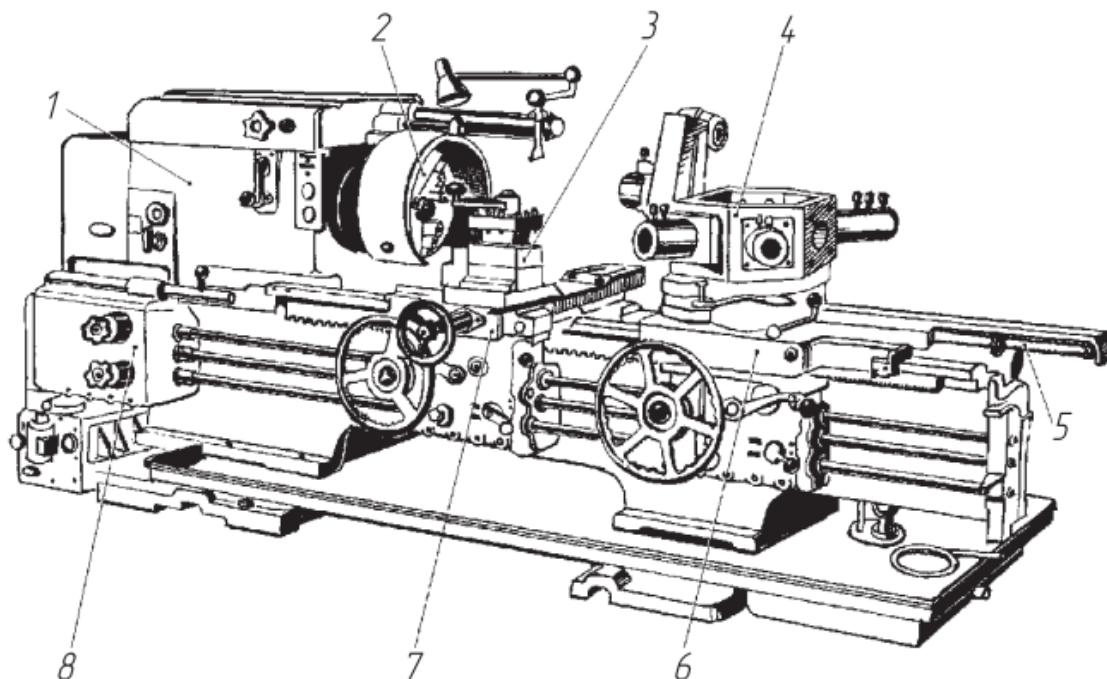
Токарно-револьверный станок модели 1П371: 1 – передняя бабка с коробкой скоростей; 2 – шпиндель с патроном; 3 – резцедержатель поперечного суппорта; 4 – револьверная головка; 5 – барабан продольных упоров; 6 – револьверный суппорт; 7 – поперечный суппорт; 8 – коробка подач.
